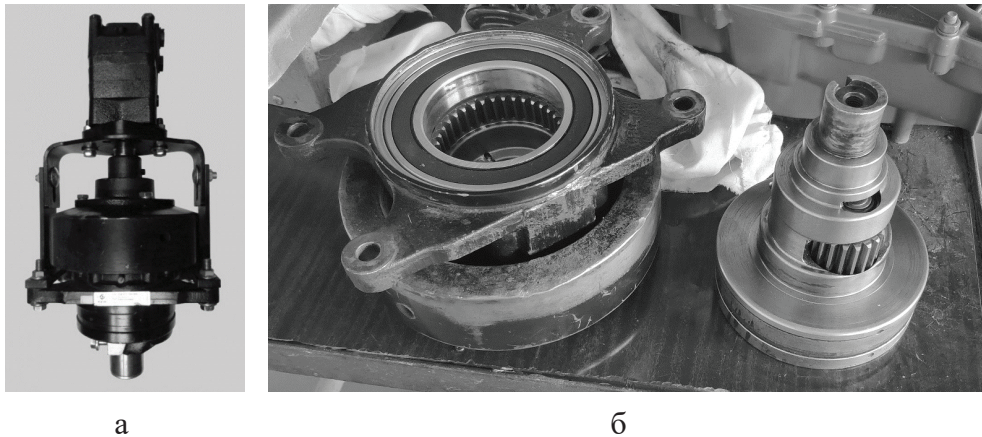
Общий вид привода Шумахера Pro-Drive 85MНv GK ASM04 для режущих аппаратов самоходной косилки КСУ-1:
